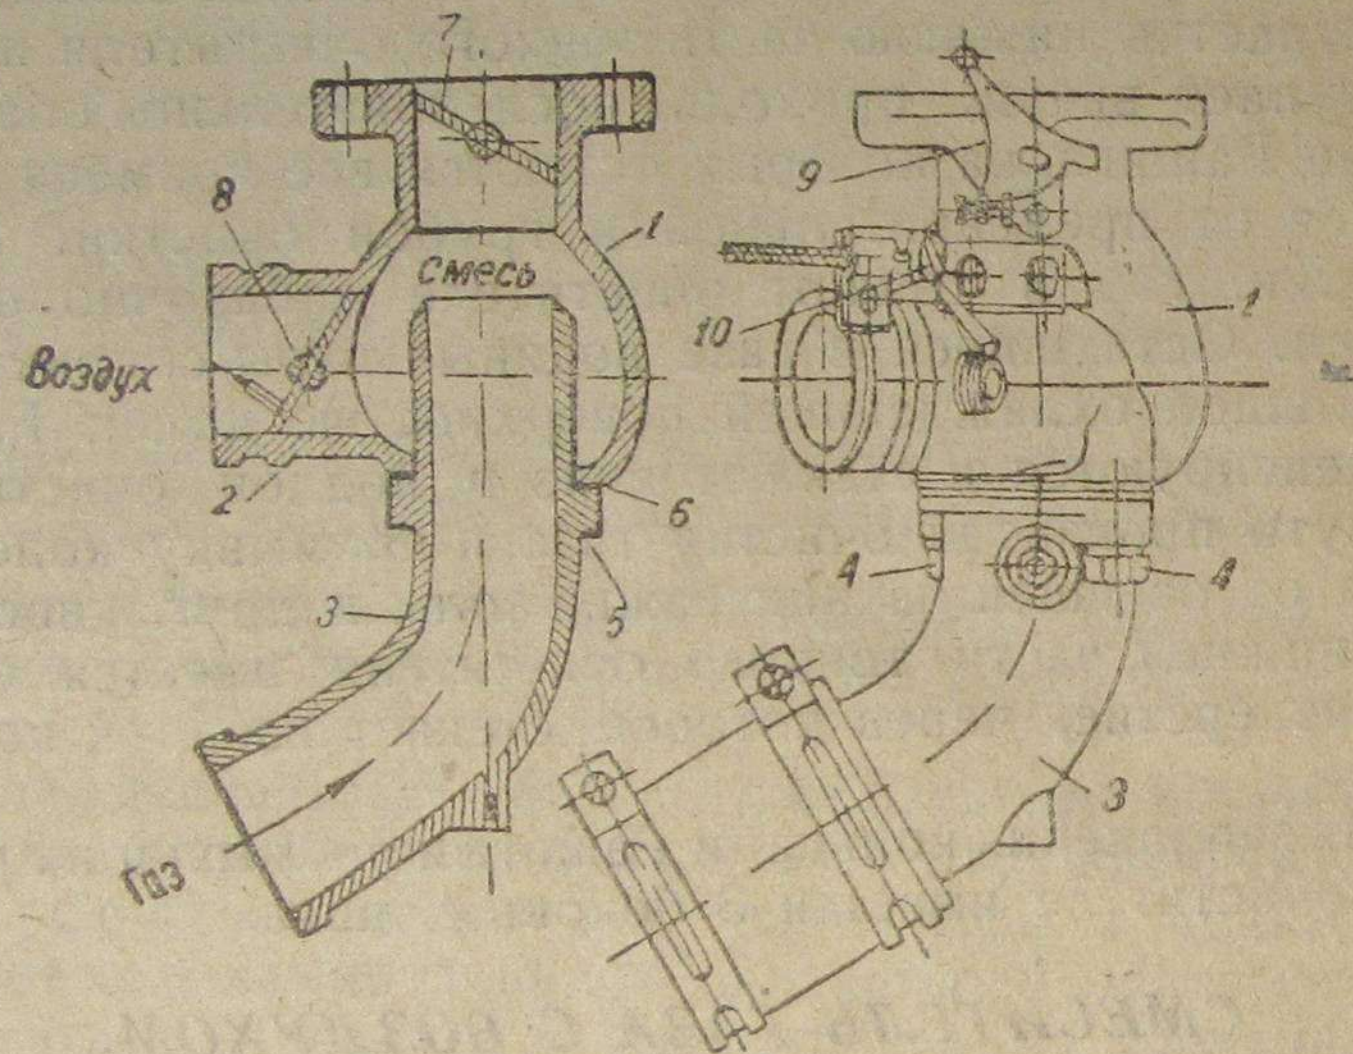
Смеситель газового двигателя ГАЗ-42:
